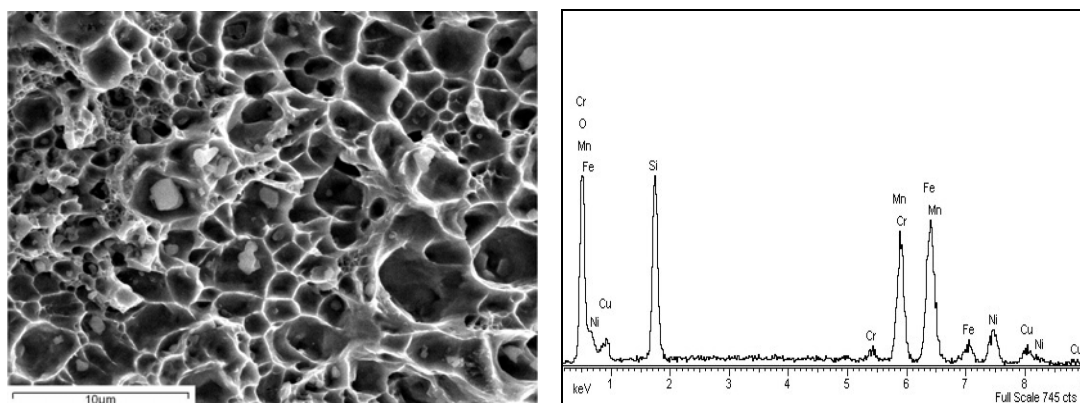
Superficie de fractura y análisis EDX de las inclusiones encontradas en la unión soldada a 875 °C durante 30 minutos.
